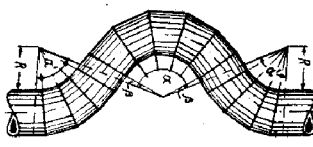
Сварная скоба, состоящая из однопипных звеньев и шести стаканов.
